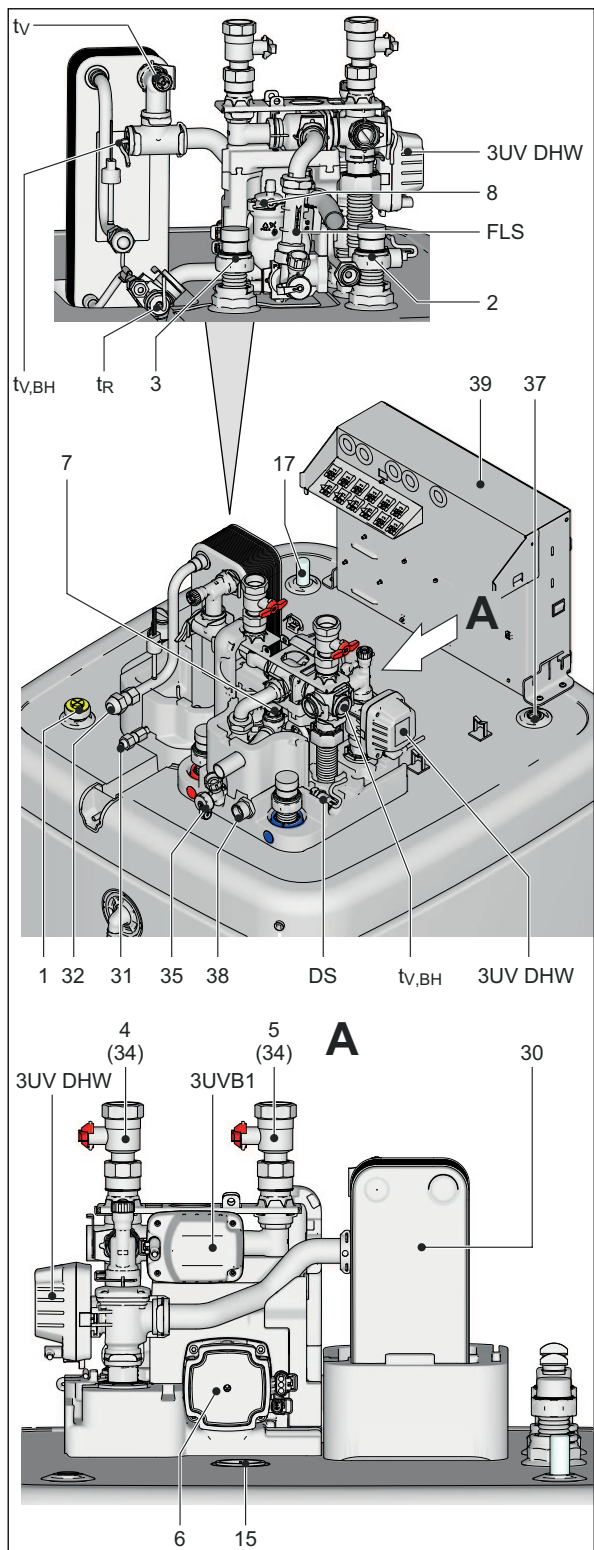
Struttura e componenti - Lato superiore dell'apparecchio⁽¹⁶⁾
